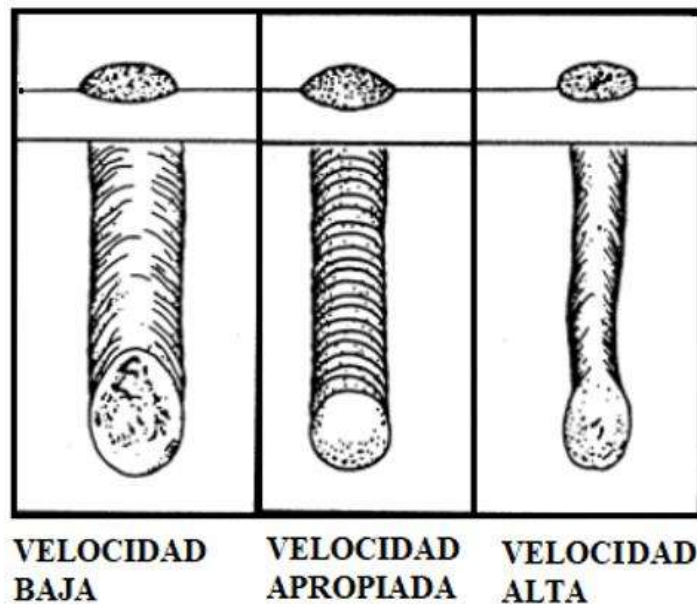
Efecto de la velocidad de avance sobre la geometría del cordón de soldadura.
